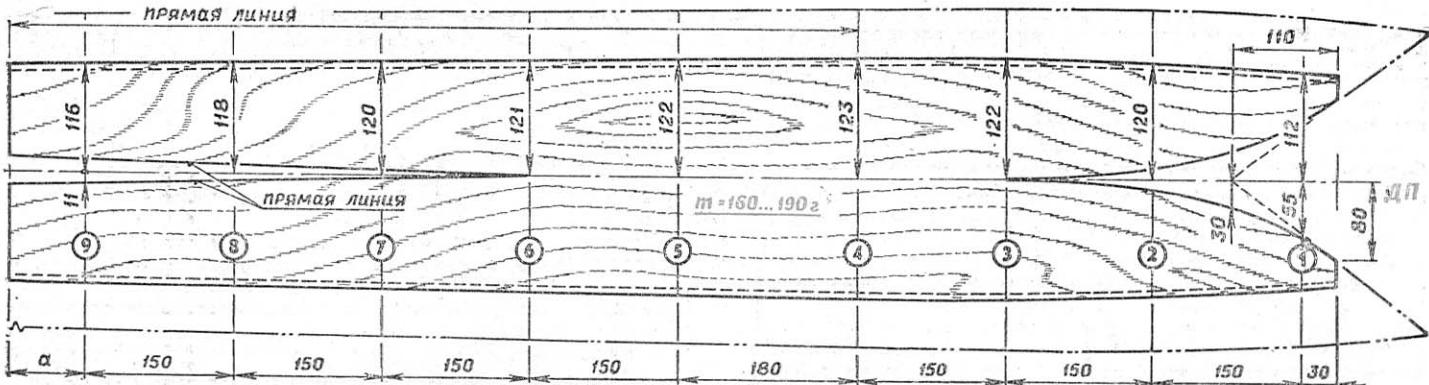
Основные размеры раскрытия листа фанеры для изготовления корпуса (размер «*a*» определить после сборки корпуса, линией условного контура показаны размеры ранее применявшихся выкройки).
